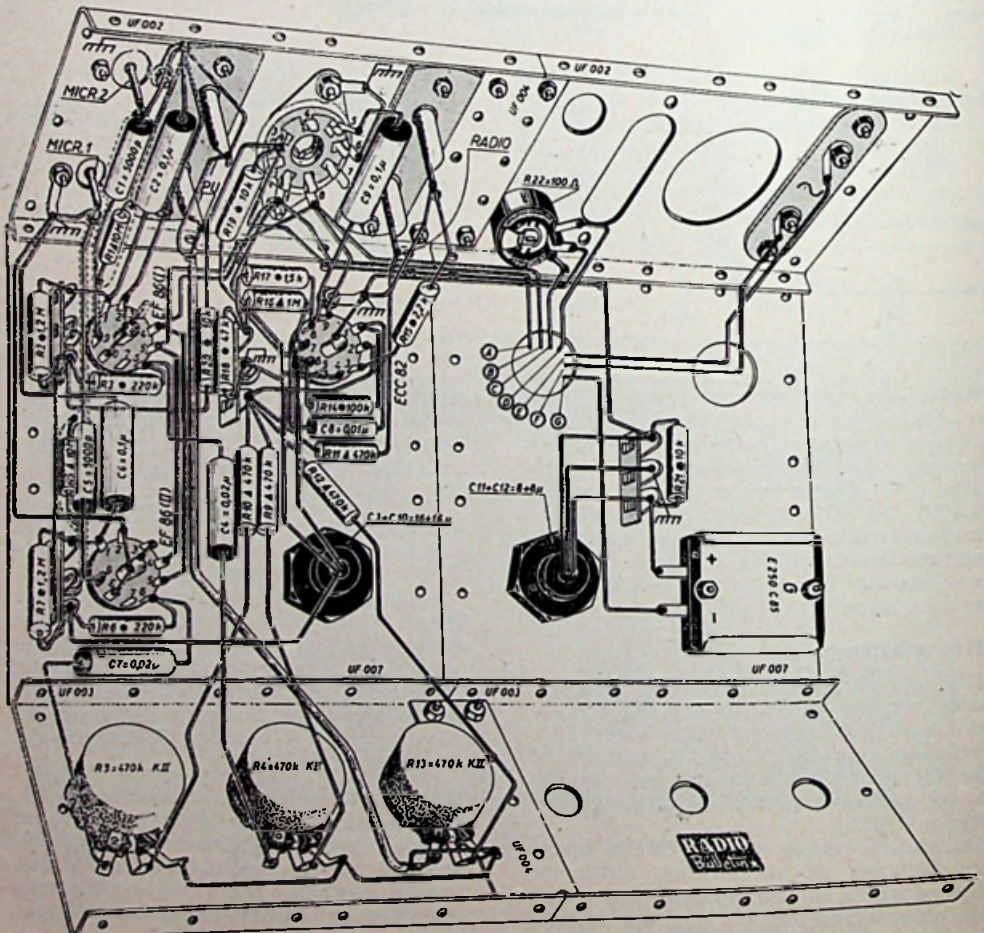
MONTAGEPLAN VAN DE UN-43
